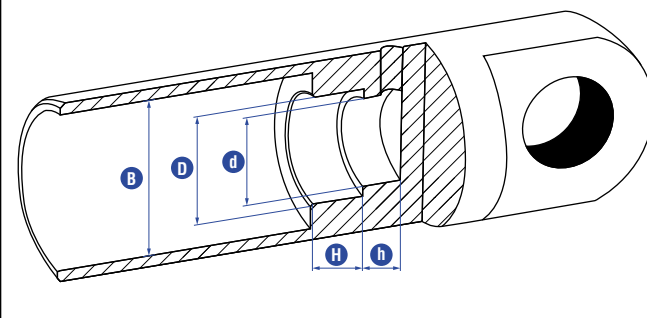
Bauraum Mindestanforderungen für Zylinder
